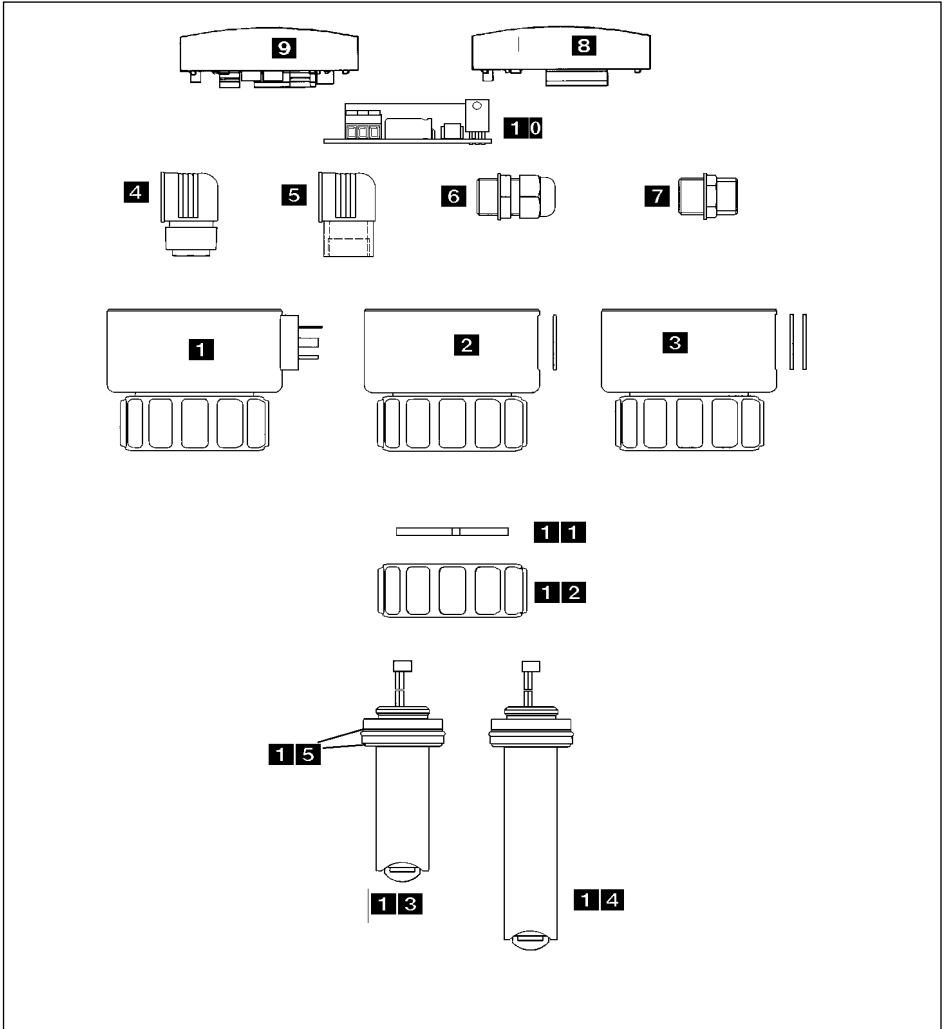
Ersatzteil-Explosionszeichnung 8025 Kompakte-Ausführung
